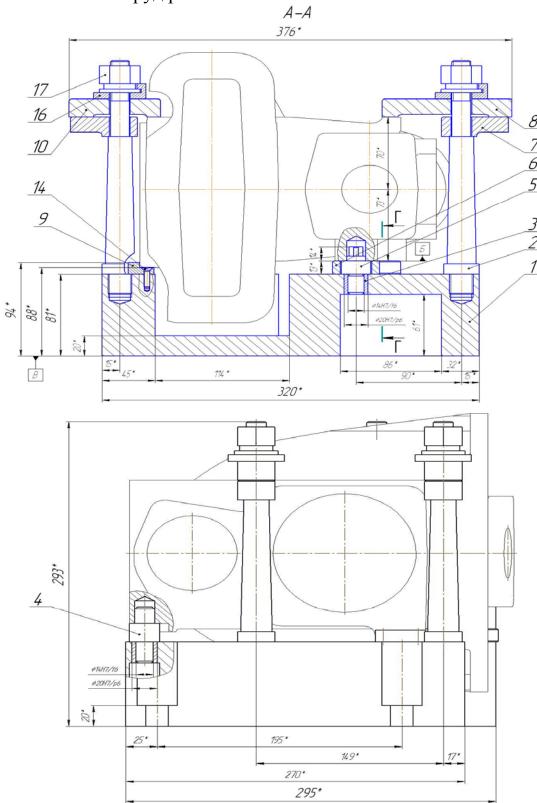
Сборочный чертеж приспособления для обрабатывающего центра ИС $-320\Pi\Phi4$  (см. также с. 193)
